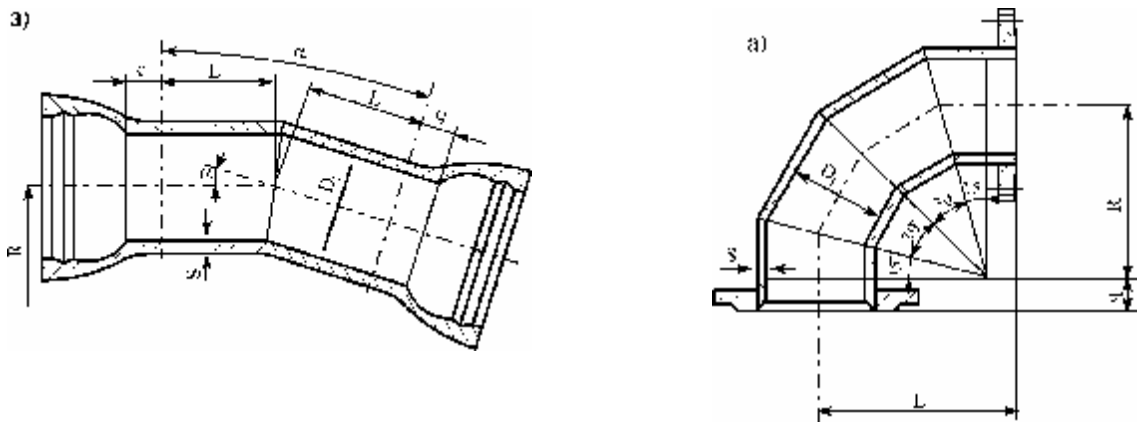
Схемы сварных отводов из высокопрочного чугуна на угол 10,15, 30 и 45 град.
